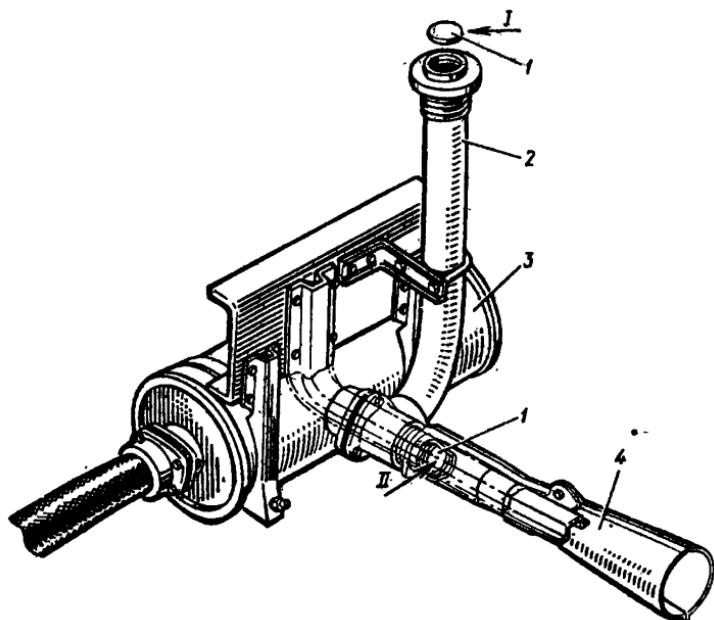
Расположение заглушки системы обогрева платформы автомобиля-самосвала мод. 6511:
